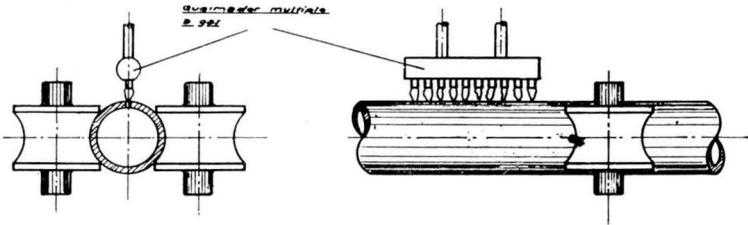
Processo de soldagem à gás na fabricação de tubos.
